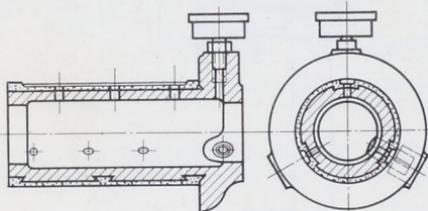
Ungeteilte Leerlaufbüchse mit Weißmetallauffläche.
